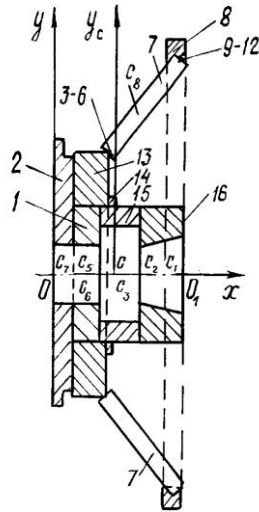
Схема фрезы И-702: 1 – пильный диск; 2 – пила; 3 – 6, 9 – 12 – крепления ножей; 7 – ножи; 8 – обод; 13 – корпус; 14 – 16 – части ступицы
